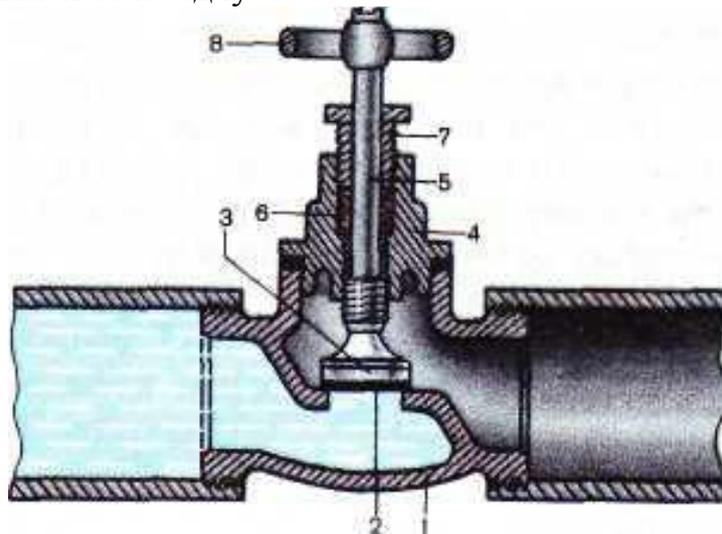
Разрез вентиля: 1 – корпус вентиля; 2 – прокладка клапана; 3 – клапан; 4 – корпус вентильной головки; 5 – шток; 6 – сальник; 7 – втулка сальника; 8 – маховик
